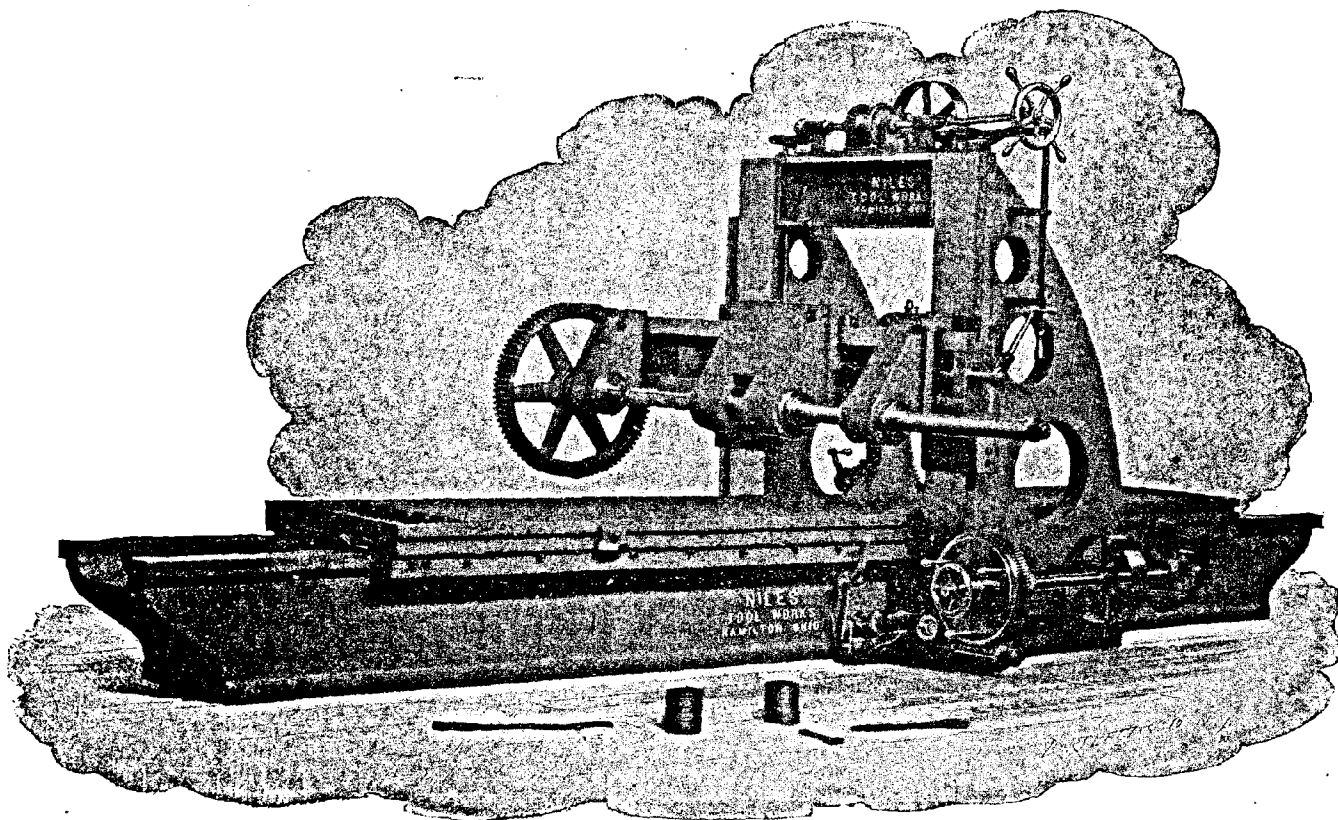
Machine à fraiser horizontale « Niles » genre raboteuse.
